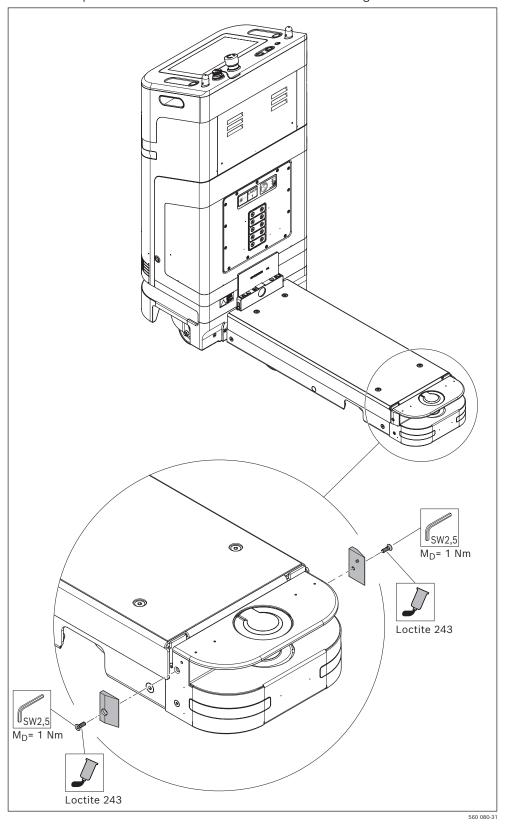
Remplacement des déflecteurs de la surface de chargement
